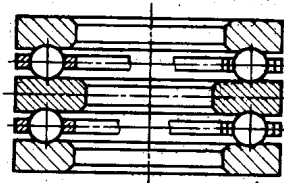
Подшипник шариковый упорный (двухрядный)
